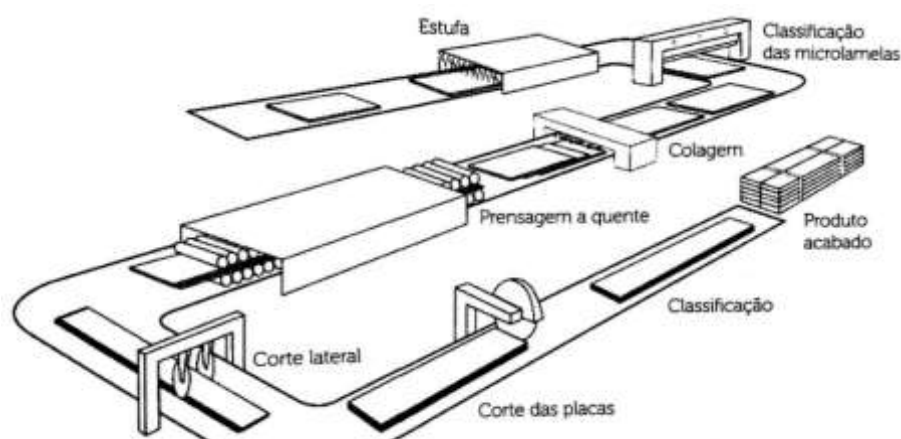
Produção de LVL. Autor: Paulo Barreto Cachim
